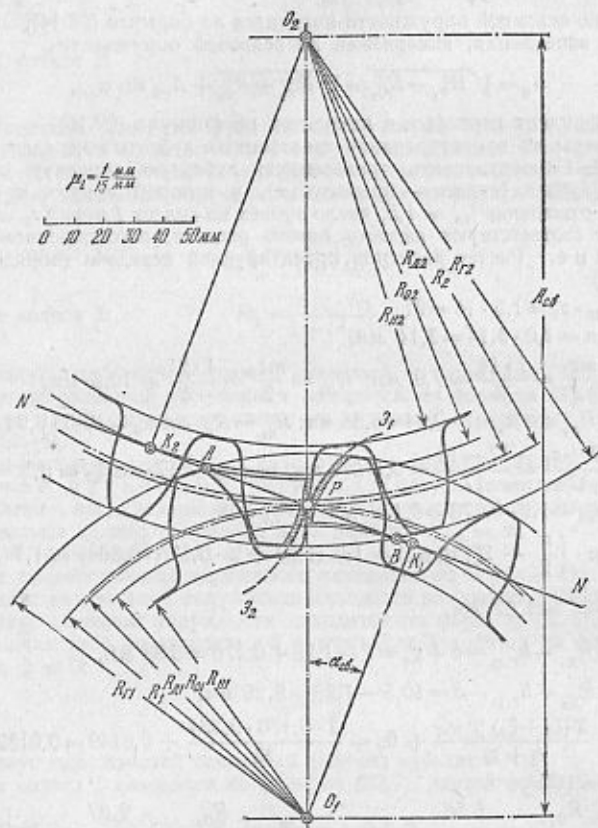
К примеру 1. Трехзвенная зубчатая передача с исправленным внешним зацеплением зубьев.
